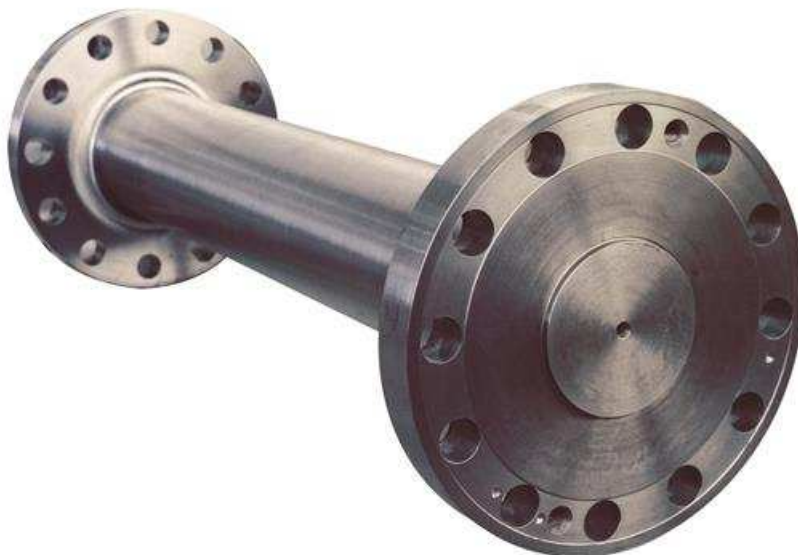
FORJADOS DE APLICAÇÃO NO SEGMENTO CIMENTEIRO
